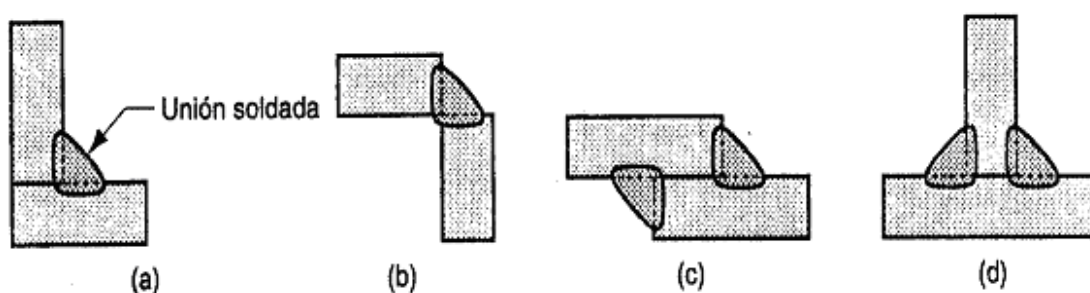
Diversas formas de soldadura de filete
